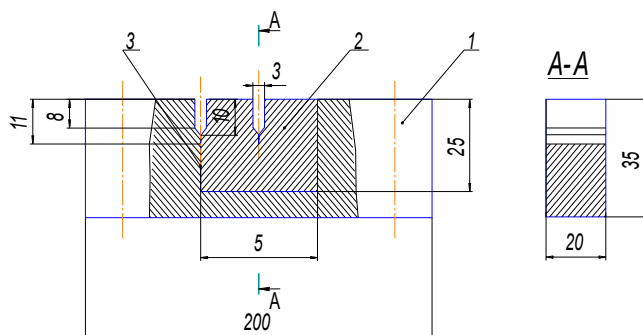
Схема нанесення бокових концентраторів у балковому зразку з напавкою: 1 – основа; 2 – зварний шов; 3 – лінія сплавлення.
